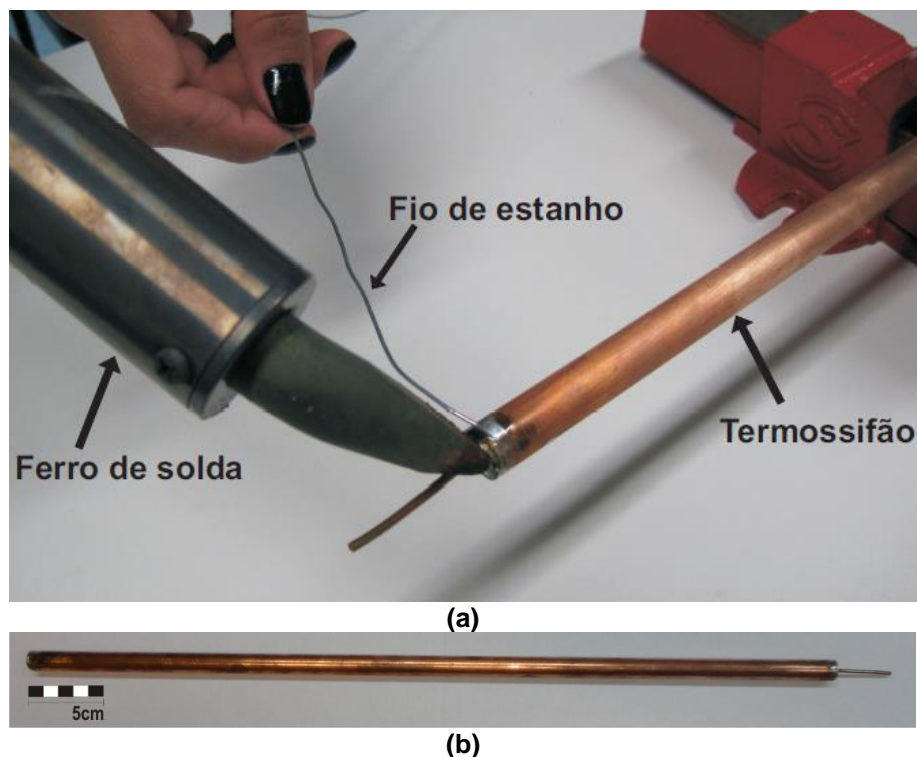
Procedimento de soldagem (a) e Termossifão soldado (b)
